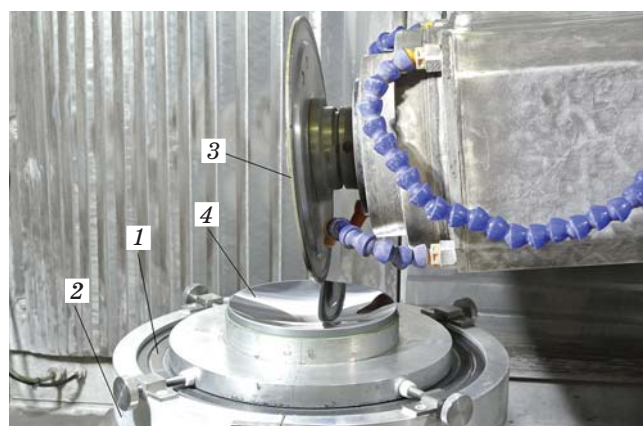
Предварительное нанесение асферической поверхности. 1 — вращающийся вакуумный стол, 2 — центрировочное приспособление, 3 — алмазная чашка, 4 — обрабатываемая линза
